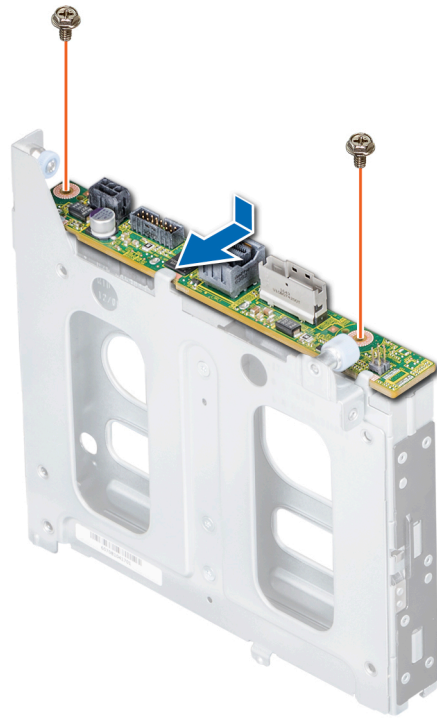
Installation du backplane arrière des disques de 2,5 pouces.
